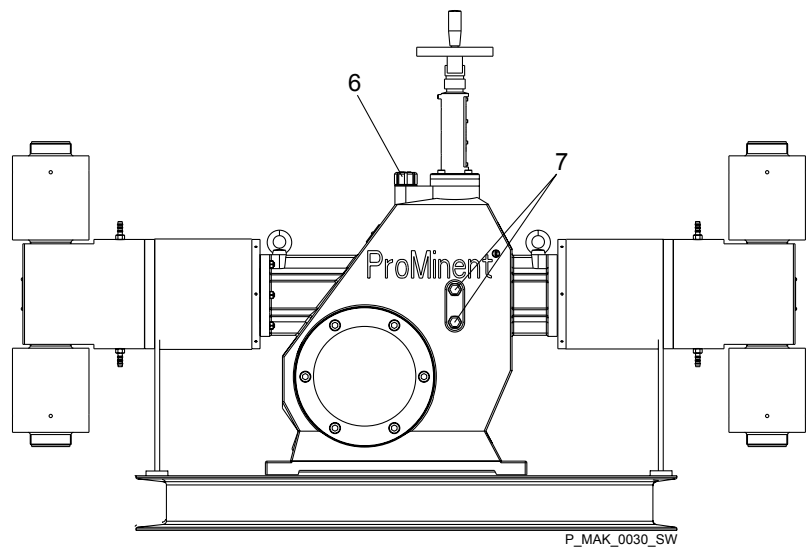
Vista del lado opuesto al motor (aquí M5Ka D)
